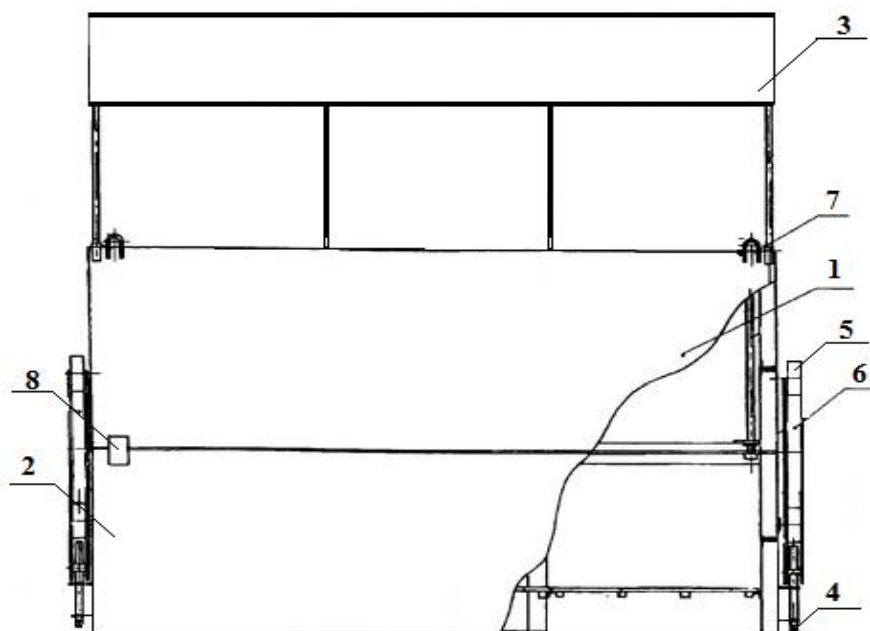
Камера ремонтная поворотная (вид сбоку)
